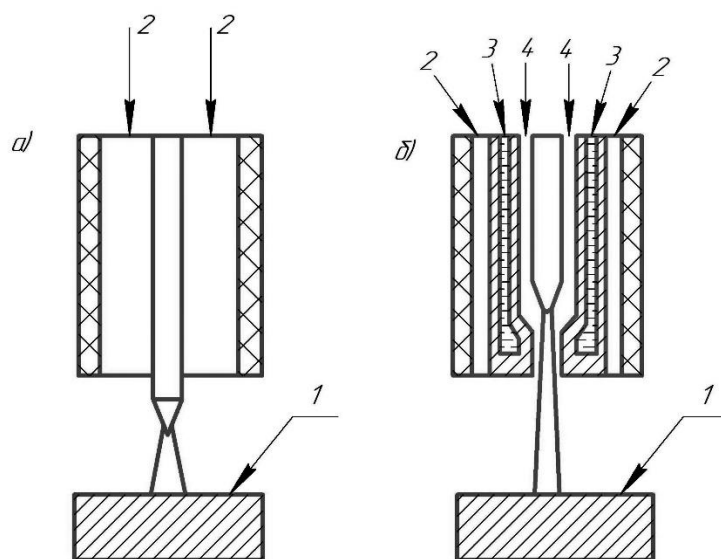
Вид сжатой дуги в процессе плазменной сварки
